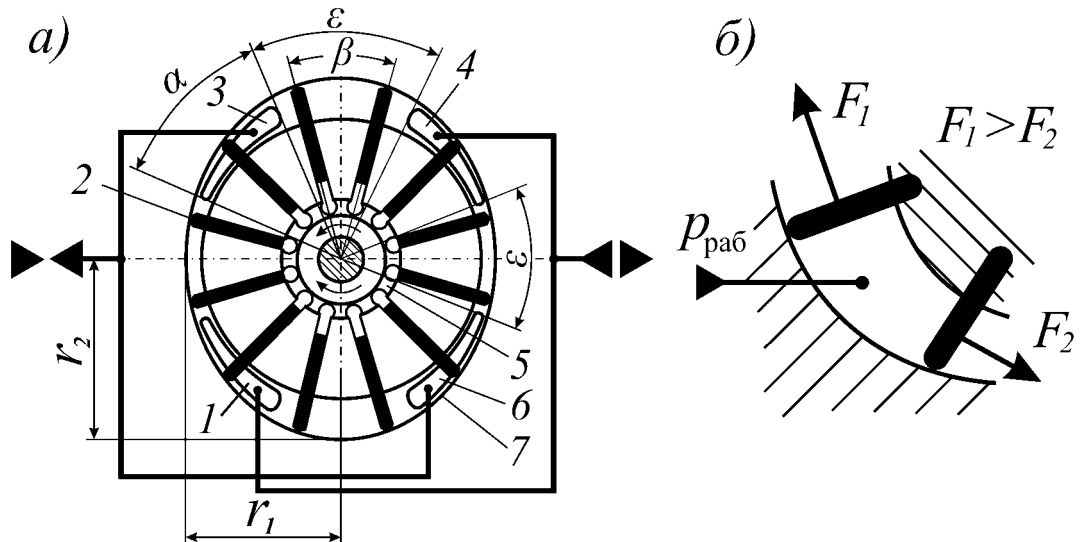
Схема пластинчатого гидромотора двукратного действия: а) основные элементы и принцип работы: 1, 3, 4, 6 – окна для подачи под рабочим давлением жидкости и ее слива; 2 – пластины; 5 – ротор с пазами под пластины; 7 – статор с эллипсным отверстием (r_1 и r_2 – меньший и больший радиусы отверстия; α – угол отверстия; β – угол между смежными пластинами; ϵ – угол между крайними стенками смежных отверстий (чтобы гарантировать отсутствие соединения зон подачи и слива $\epsilon > \beta$); б) схема образования окружной силы при подаче жидкости под рабочим давлением $p_{\text{раб}}$ в рабочую камеру: F_1 и F_2 – силы, возникающие от давления рабочей жидкости на две пластины одной рабочей камеры
